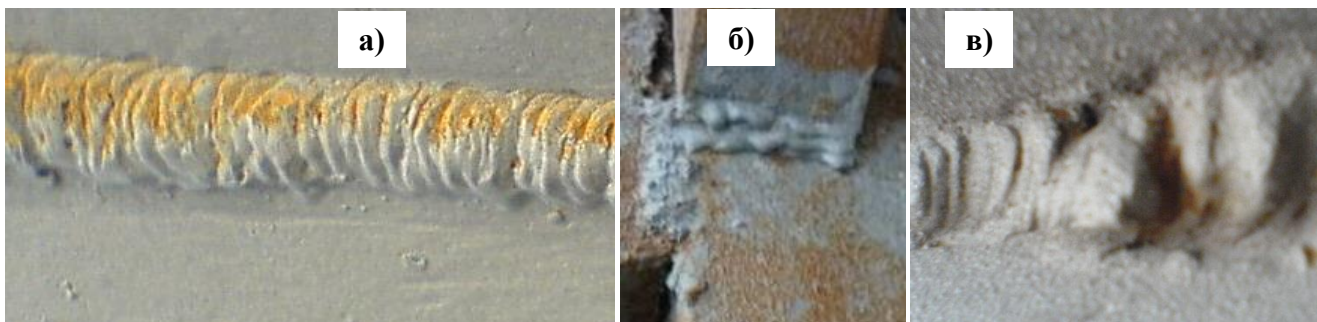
Грубая поверхность сварного шва:
